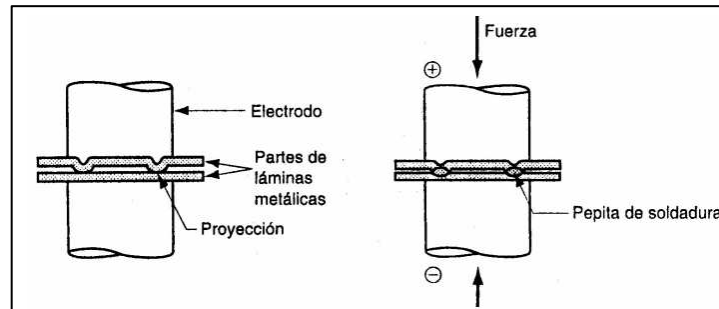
Soldadura por resistencia de protuberancia
